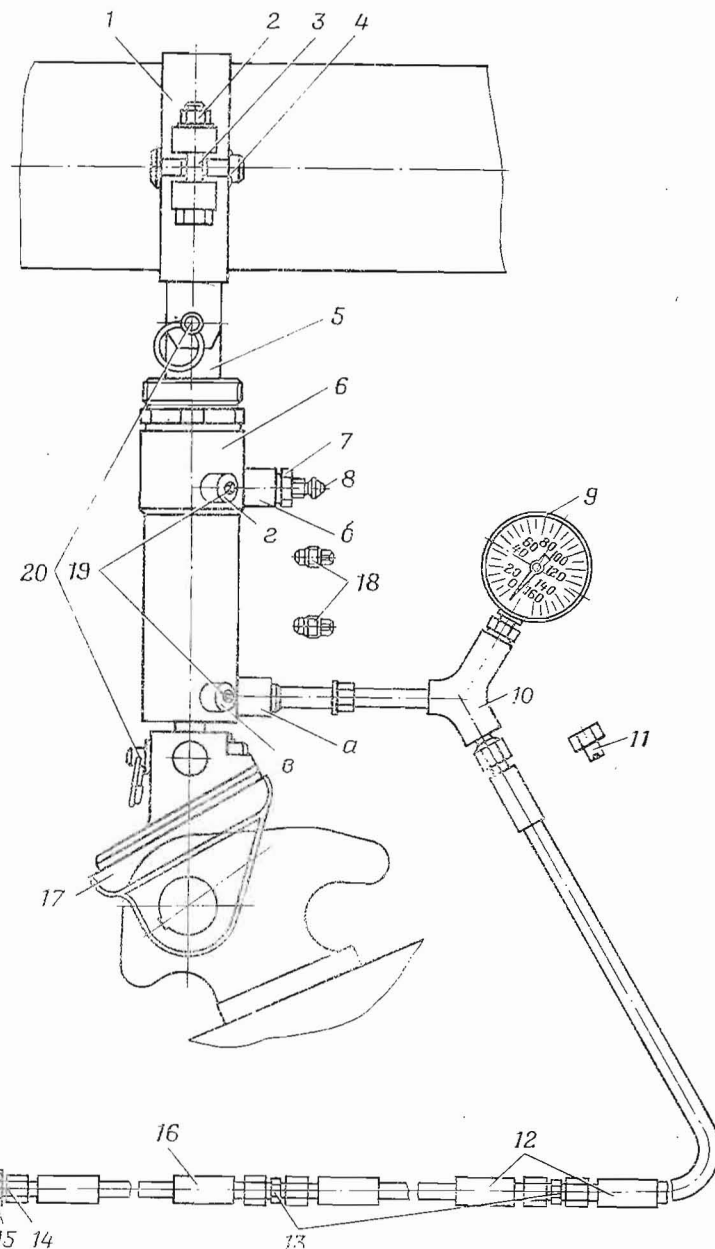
Проверка момента срабатывания сдающего звена подъемного механизма:
